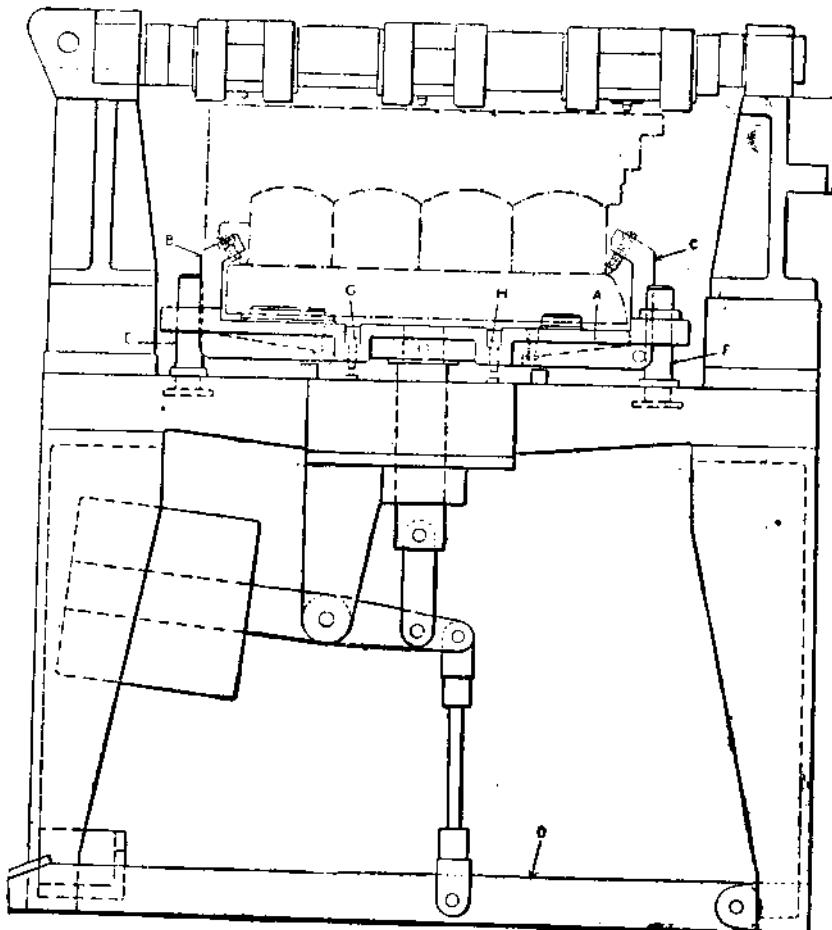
Специальный станок Форда для заливки подшипников баббитом.
